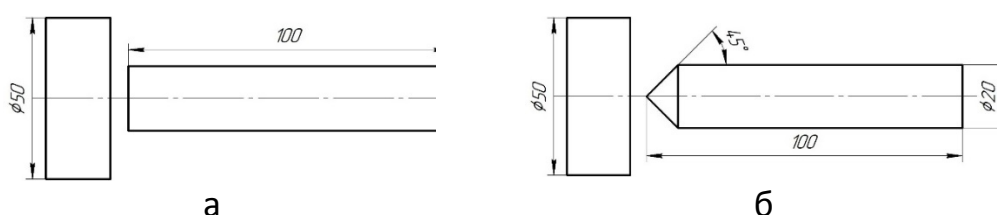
Эскиз болтов, а – без подготовки контактирующих поверхностей; б – с конической контактирующей поверхностью
